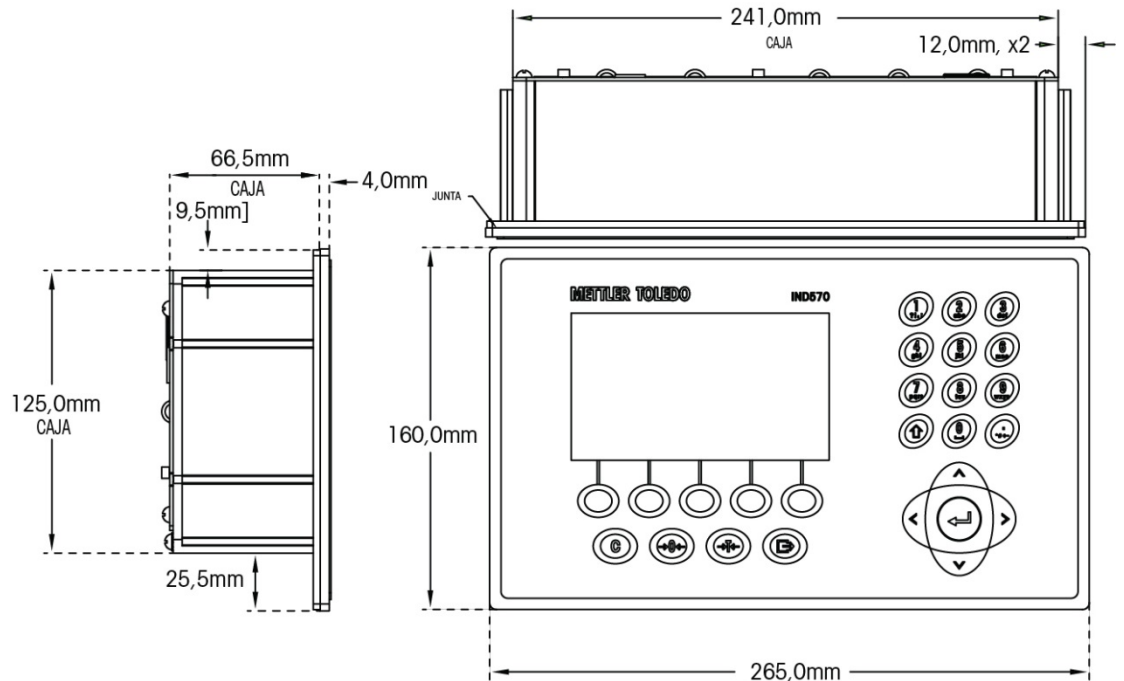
dimensiones de la caja de montaje en panel del IND570
